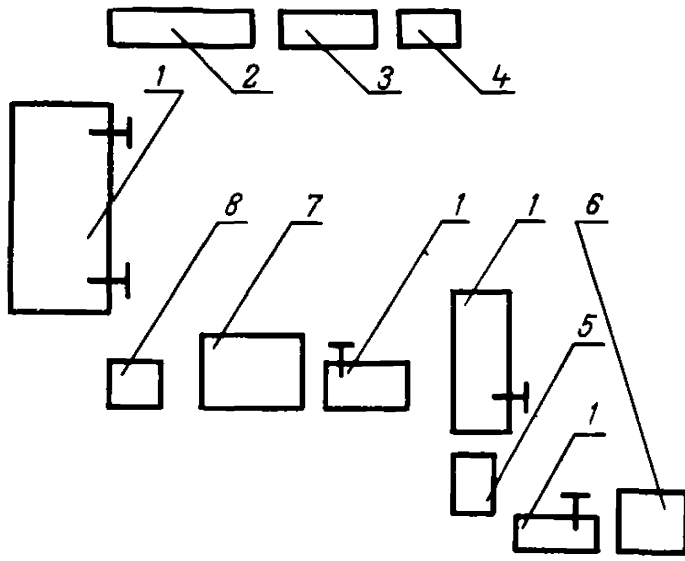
Типовая схема планировки рабочего места разборки и сборки узлов двигателя:
